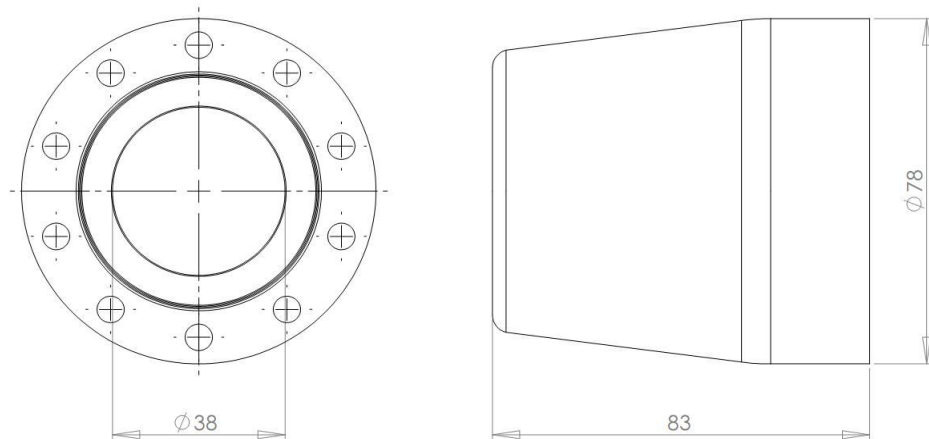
Geometria proposta para o cone (dimensões em mm)
